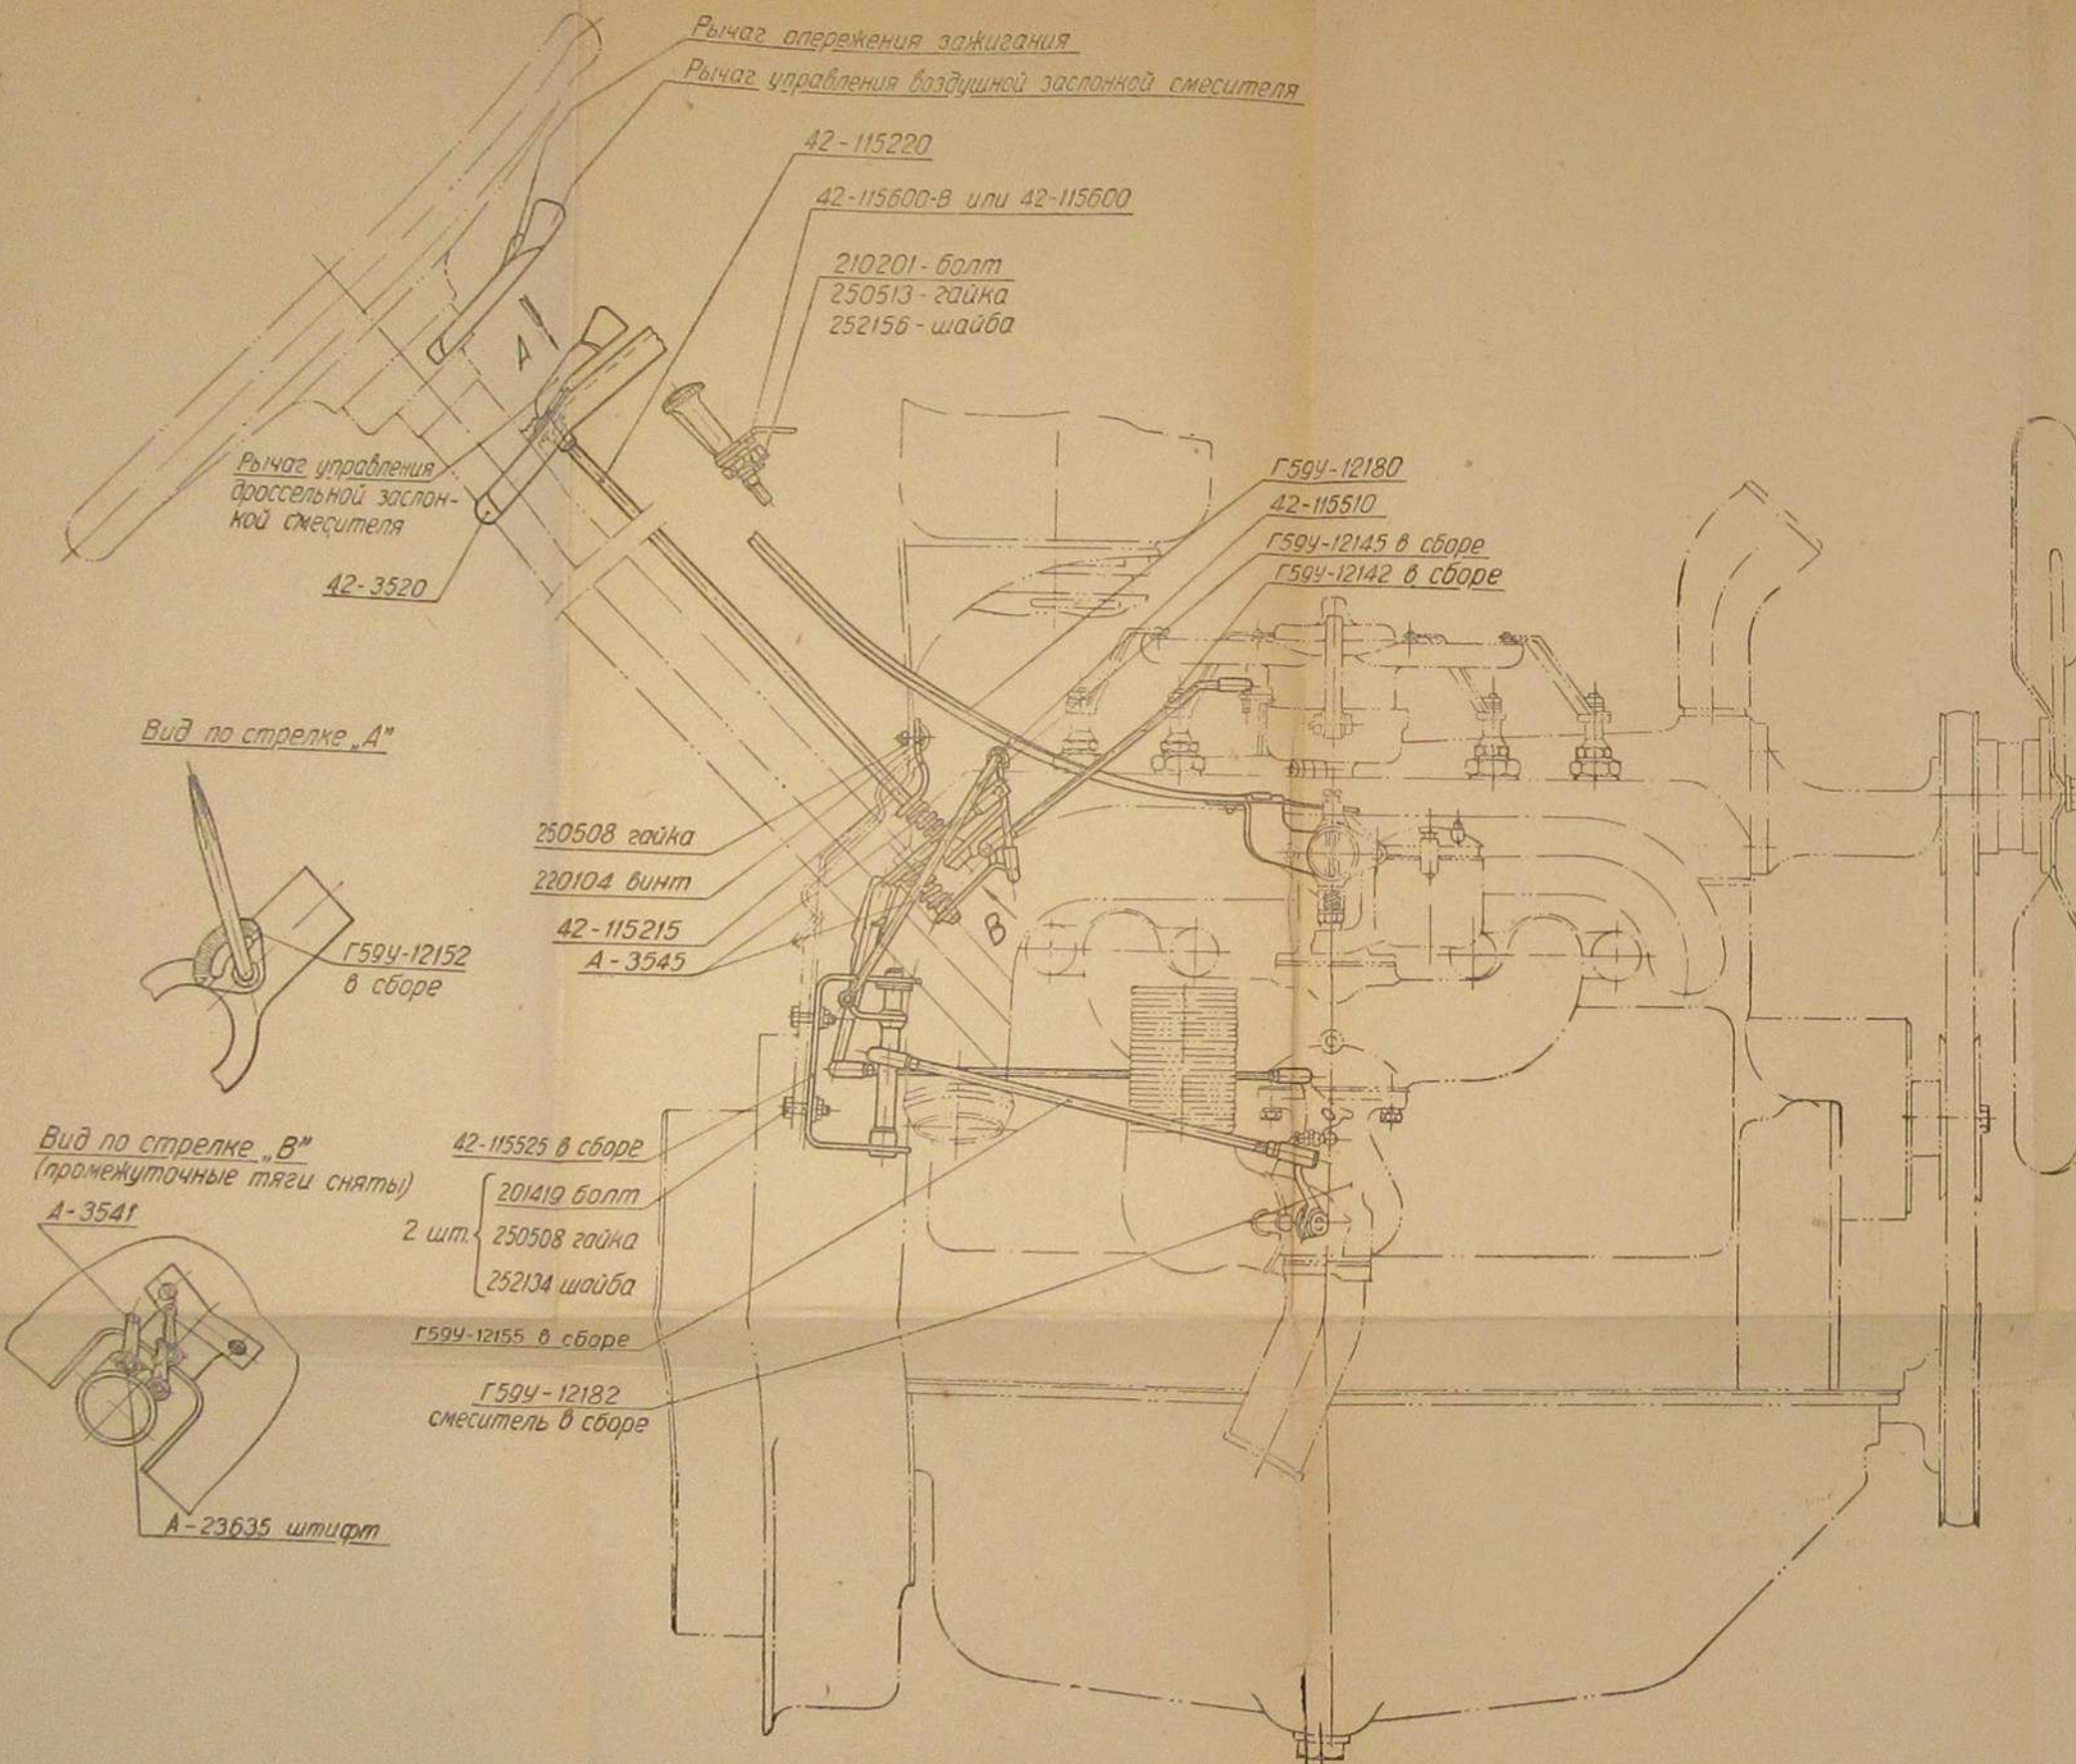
Управление смесителем и карбюратором двигателя ГАЗ-42 (вид сбоку).
